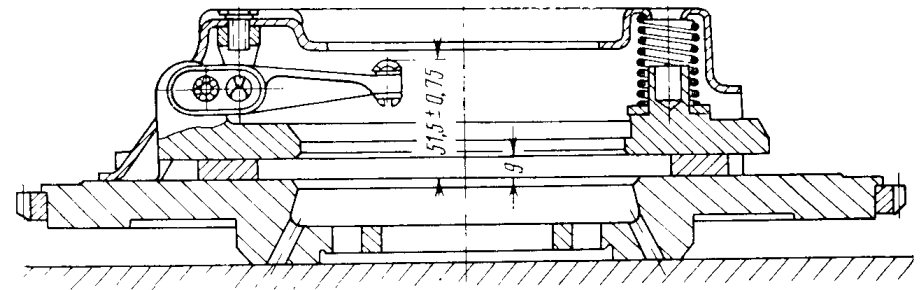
Установка на маховик нажимного диска с кожухом для регулировки рычагов
